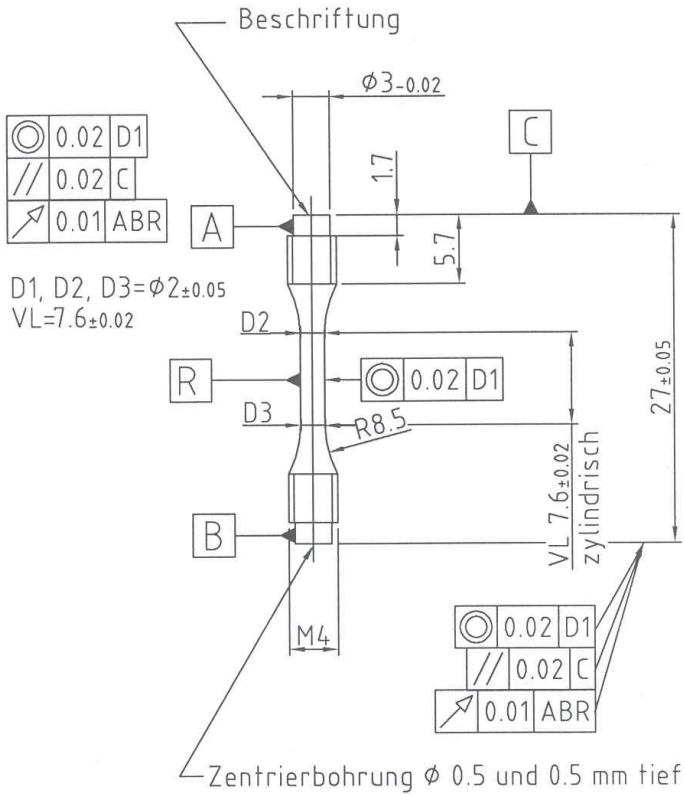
Technische Zeichnung der miniaturisierten LCF-Probe mit Gewinde.
